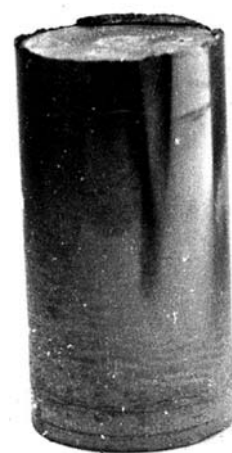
Заготовка с нанесенным на нее слоем обмазки
